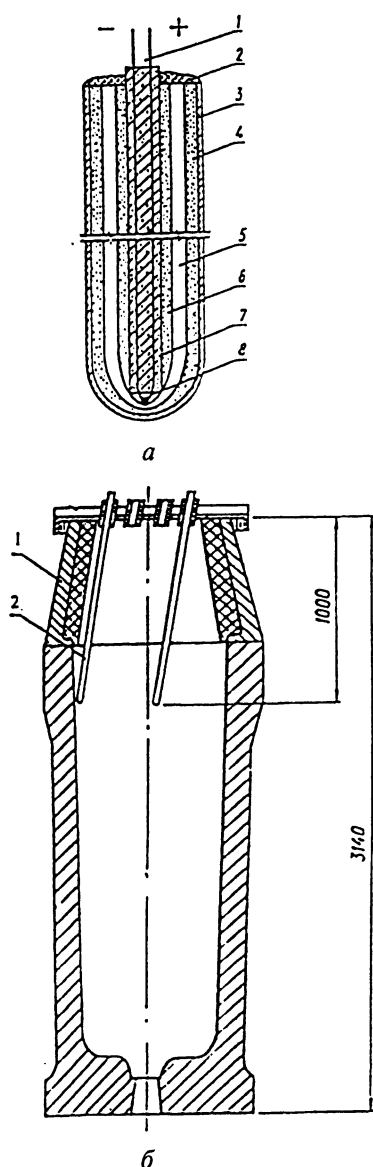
Схема термодатчика (а) и экспериментальная изложница в сборе (б): а — 1 — свободные концы; 2 — замазка; 3 — внешний чехол; 4 — графитовый порошок; 5 — внутренний кварцевый кожух; 6 — алундовая засыпка; 7 — алундовая двухканальная засыпка; 8 — спай термопары ВР 5/20; б — 1 — прибыльная надставка; 2 — термодатчик
